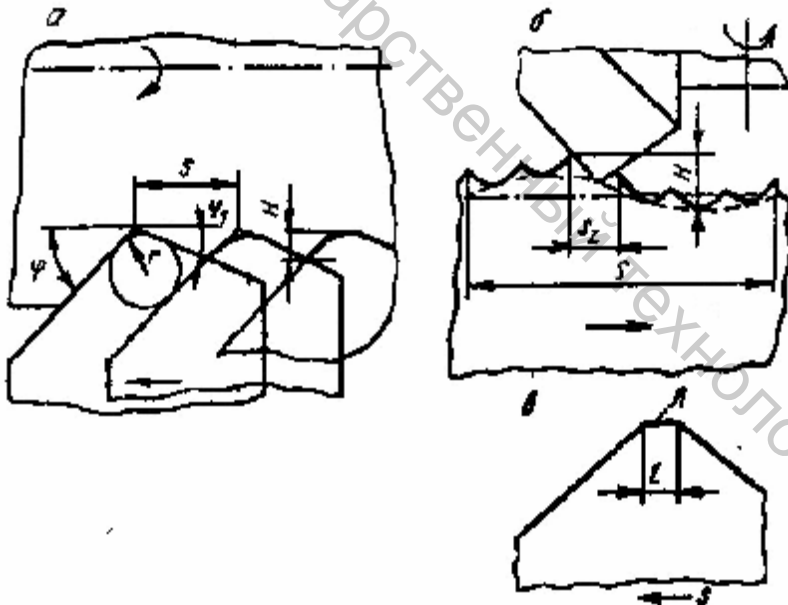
Формирование «геометрической» шероховатости при точении (а), торцовом фрезеровании (б) и резец с дополнительным режущим лезвием (в)
